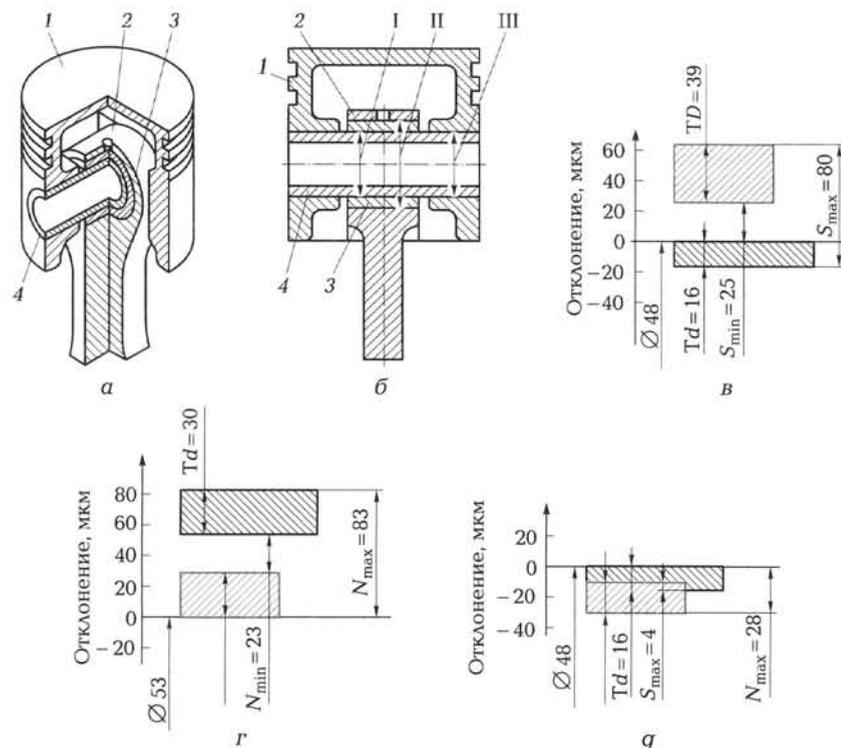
Поршневая группа в сборе (а, б) и схемы расположения полей допусков валов и отверстий соединений с зазором (в), с натягом (г), по переходной посадке (д):
